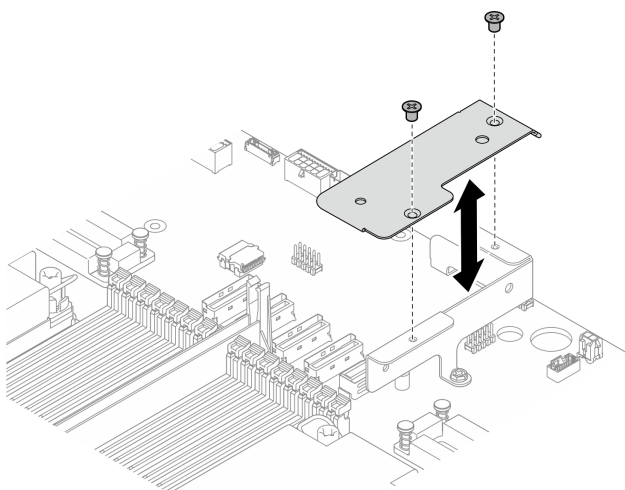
Extracción e instalación de la cubierta central de la guía de cables
